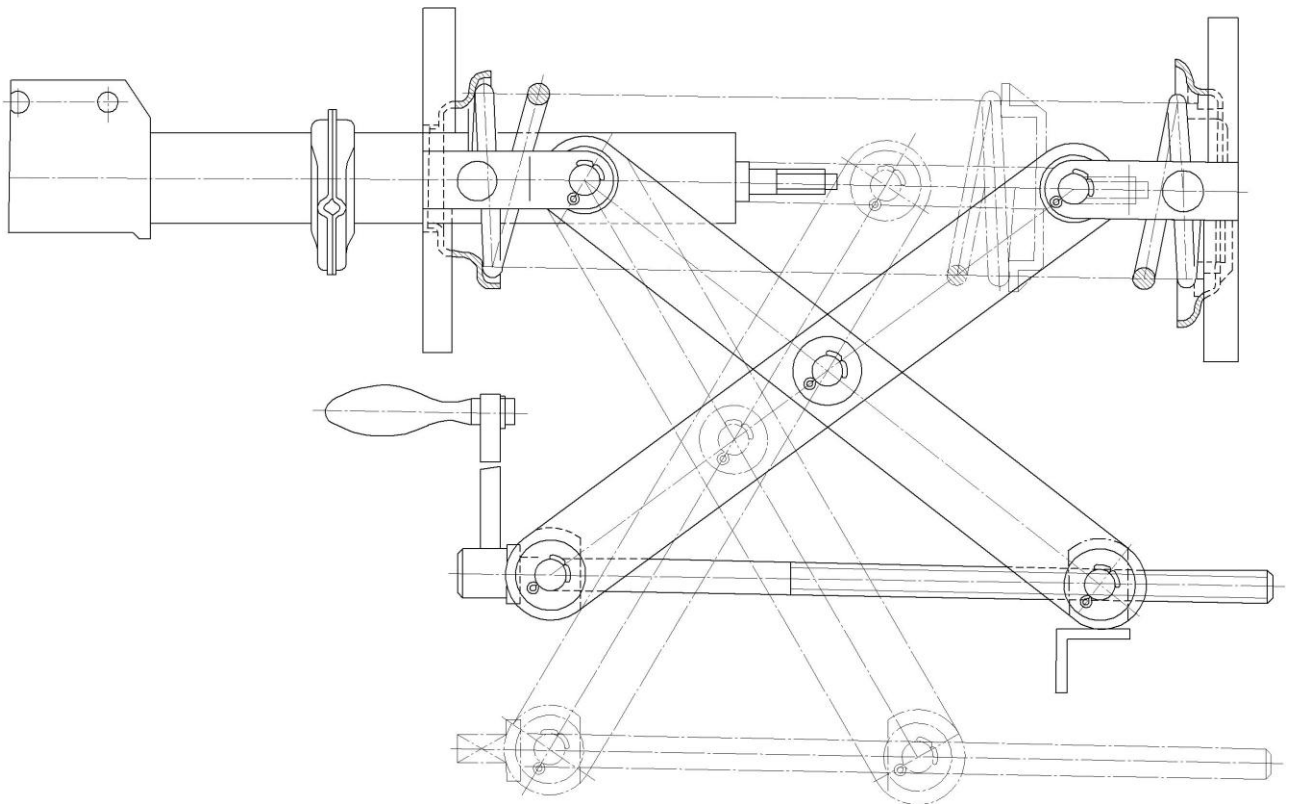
Приспособа для складання пружини зі стійкою передньої підвіски
